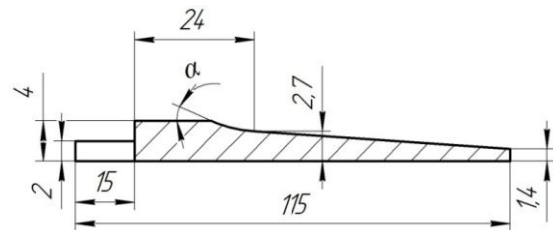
Схема профілю поперечного перерізу витка ШГЗ
